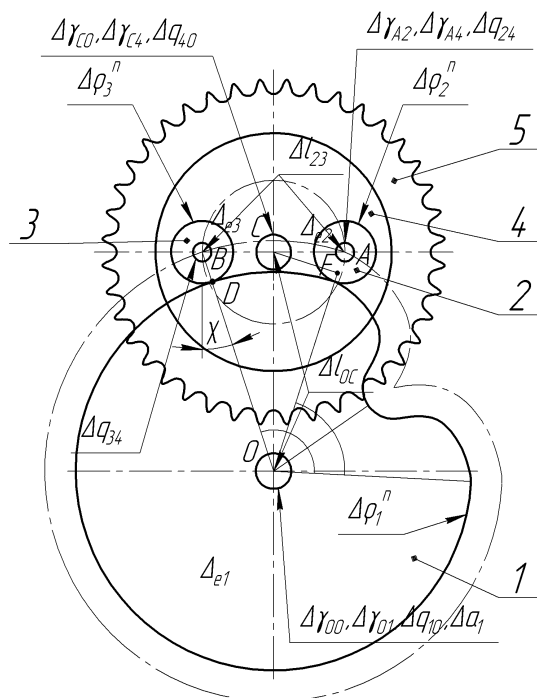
Схема крокового механізму привода транспортувальної системи
